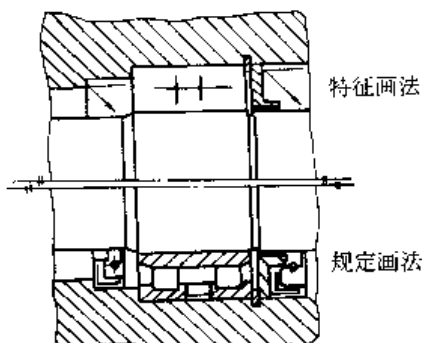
双列圆柱滚子轴承在装配图中的画法
